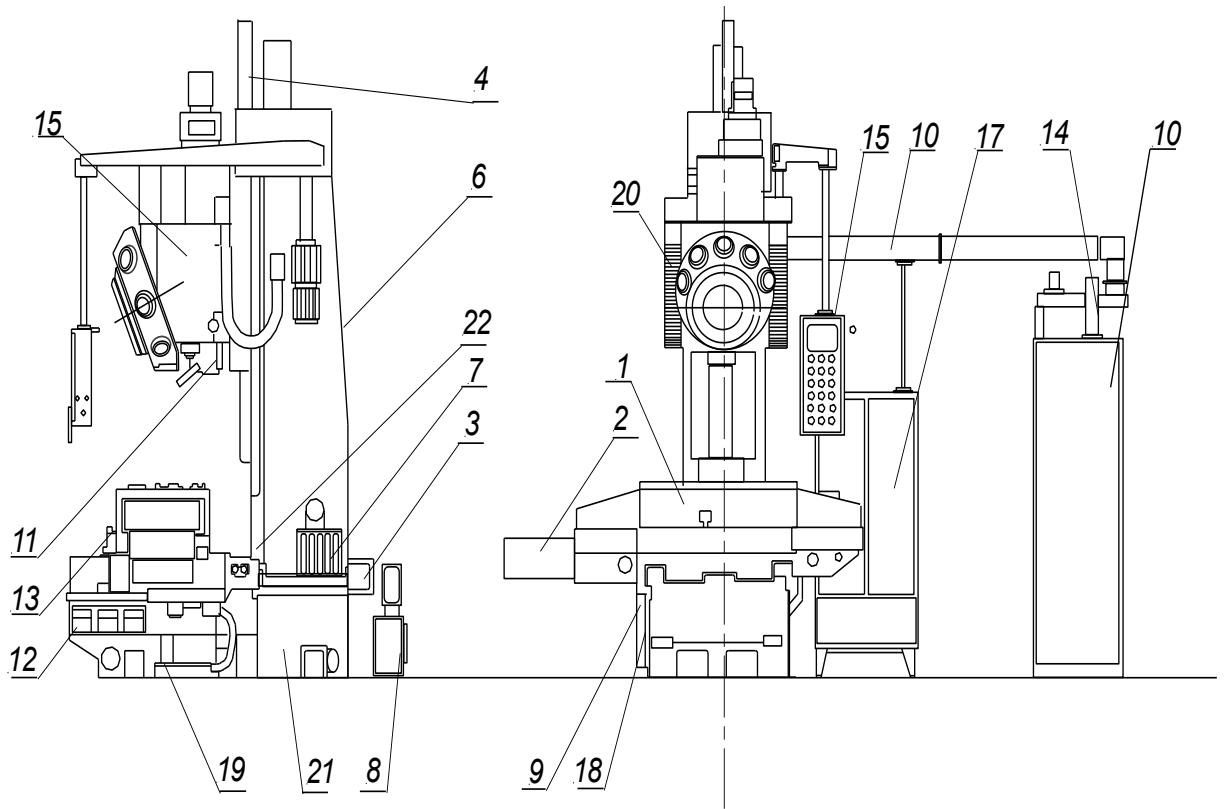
Схема вертикального фрезерного верстата МА655А7
